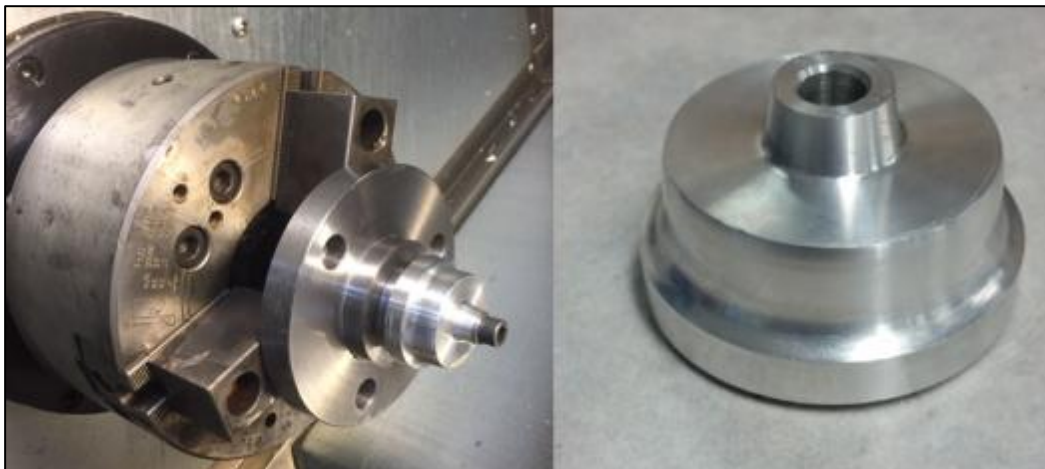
Preforma terminada para maquinado de turbo [fuente propia]
